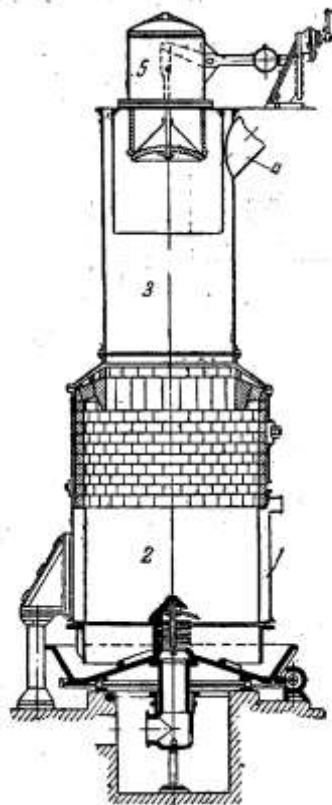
Механізований газогенератор. 1- шахта; 2-сталеві лопатки; 3- гідравлічний затвор; 4-завантажувальний пристрій; 5- газопровід; 6 - шуровочний пристрій; 7-чаша
